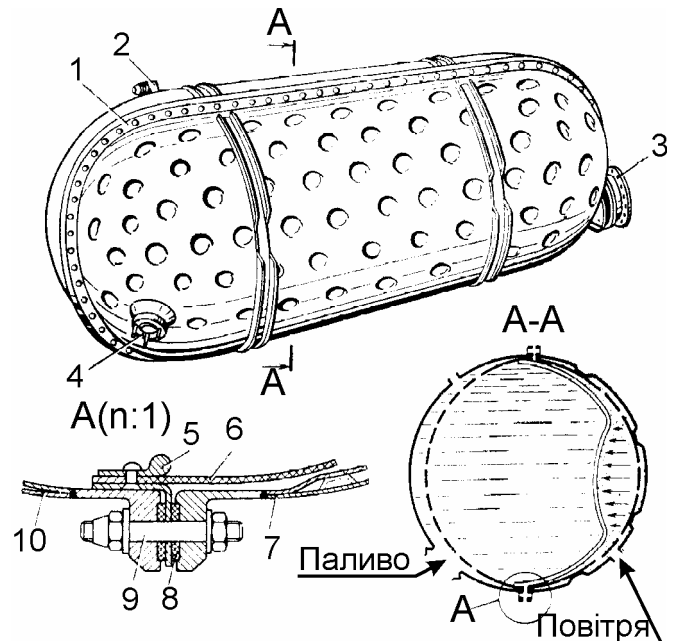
Паливний акумулятор (МиГ-25): 1 — фланець; 2 — штуцер повернення палива до насоса; 3 — штуцер паливної магістралі; 4 — штуцер наддування; 5 — профіль; 6 — мембрана; 7 — повітряна оболонка; 8 — ущільнювальна прокладка; 9 — болт; 10 — паливна оболонка
